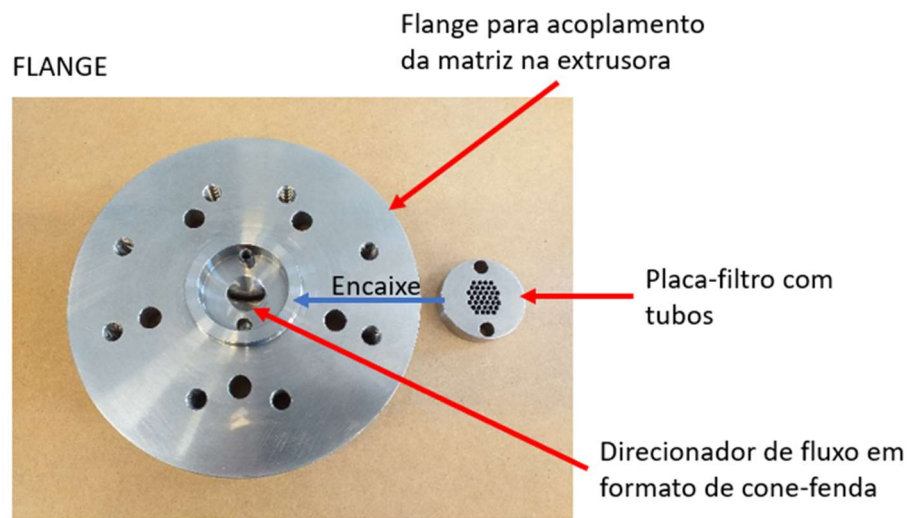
Flange com detalhe do direcionador de fluxo e placa filtro.
